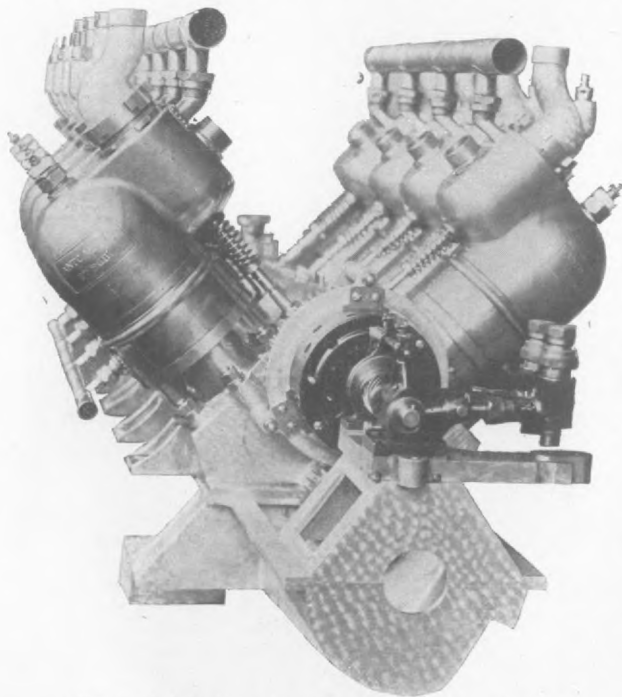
Antoinettemotor mit geschmiedeten Zylindern und galvanoplastisch hergestellten Kupfermänteln.
